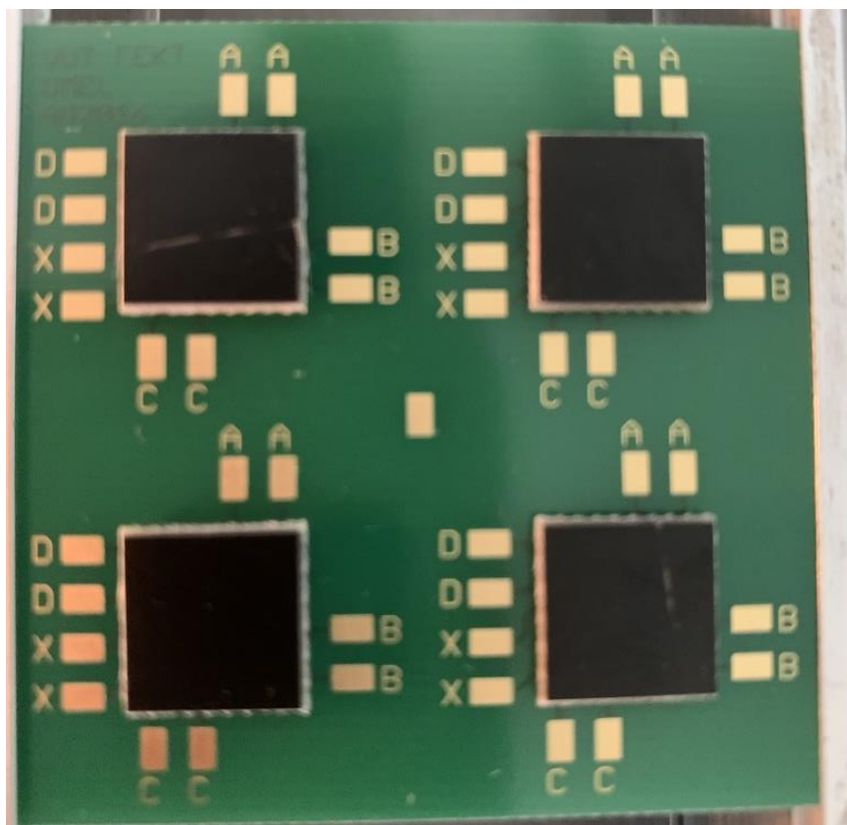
Před sesouhlasením testovacího BGA pouzdra a testovací DPS
